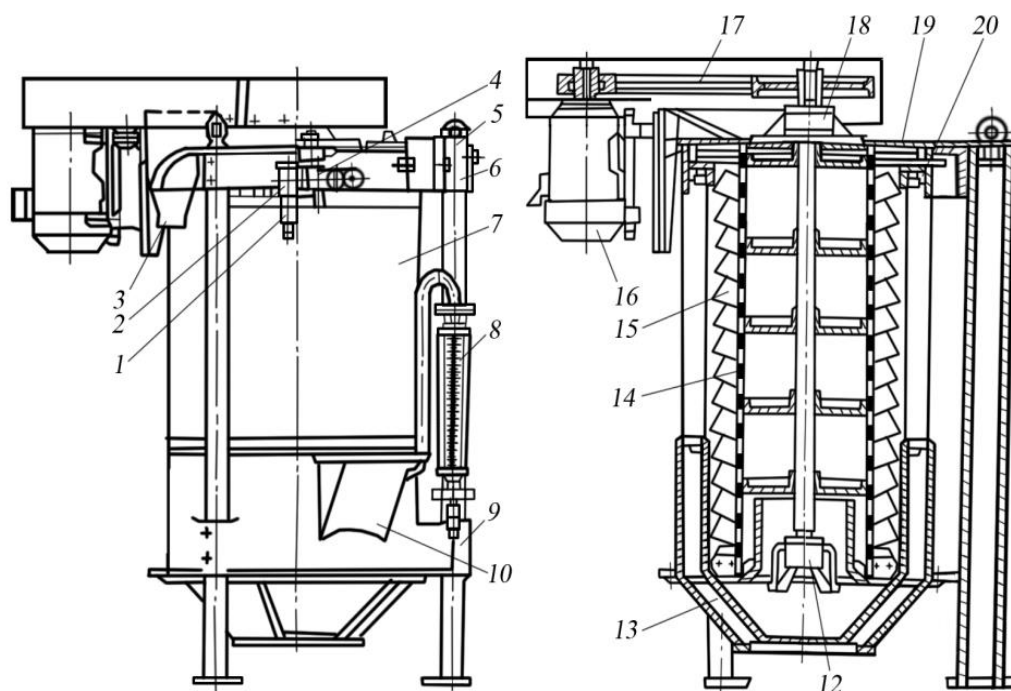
Машина А1-БМШ для мокрого шелушения зерна: 1 — запорный вентиль; 2 — фильтр; 3 — выпускной патрубке; 4 — мембранный вентиль; 5 — командный прибор; 6 — траверса; 7 — кожух; 8 — ротаметр; 9 — корпус; 10 — приемный патрубке; 11 — стойка; 12, 18 — нижний и верхний подшипниковые узлы; 13 — конус; 14 — ситовой цилиндр; 15 — ротор; 16 — электродвигатель; 17 — клиноременная передача; 19 — крышка; 20 — трубчатое кольцо.
